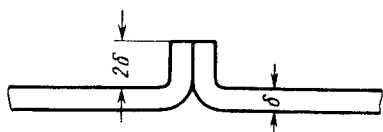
Подготовка кромок при толщине металла до 2-х мм
